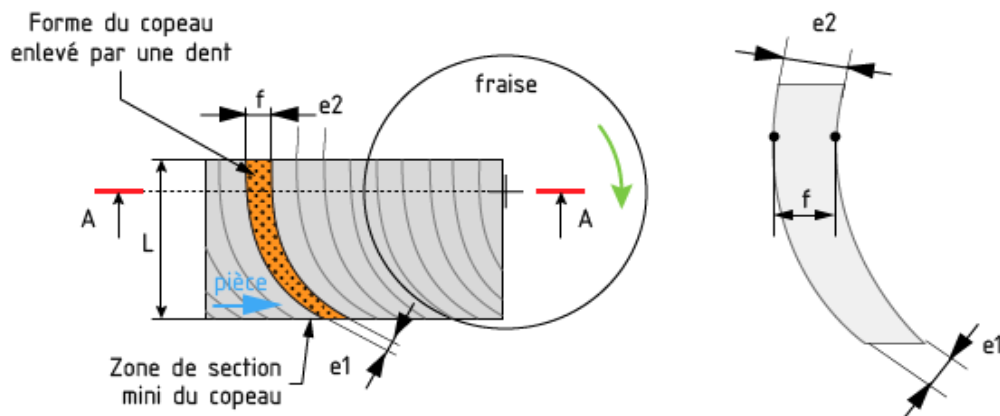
La forme du copeau enlevé par une dent pour le fraisage en bout [15].
